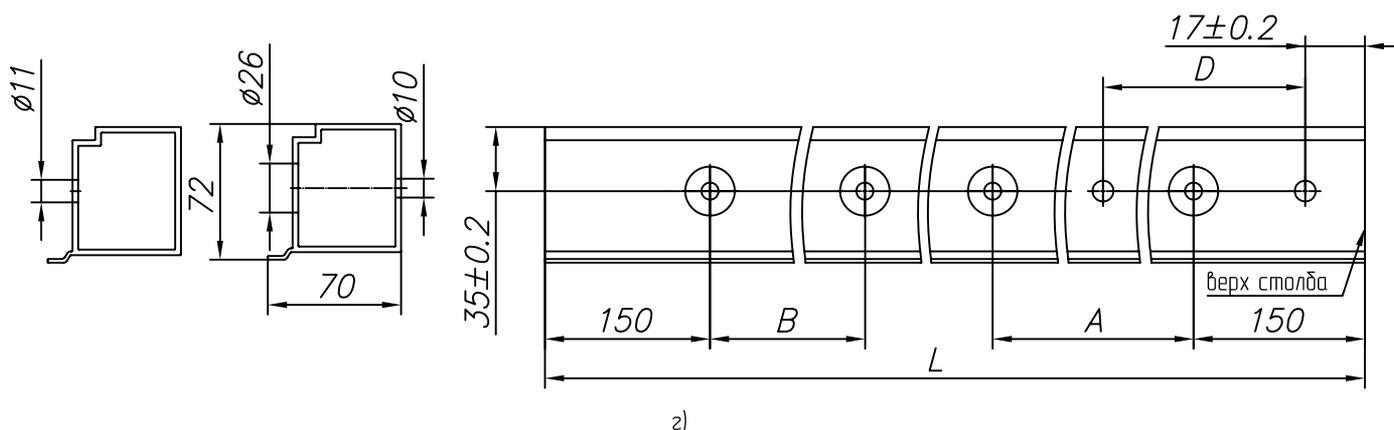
Изготовление столба FLGU.400.0502 при встроенном монтаже калитки:
